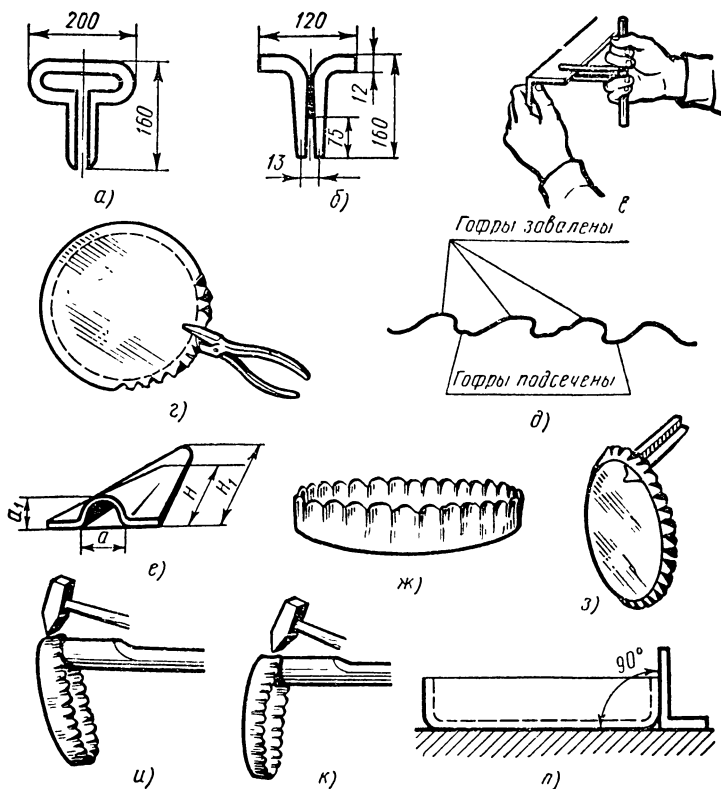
Посадка металла при изготовлении дна ручным способом:
